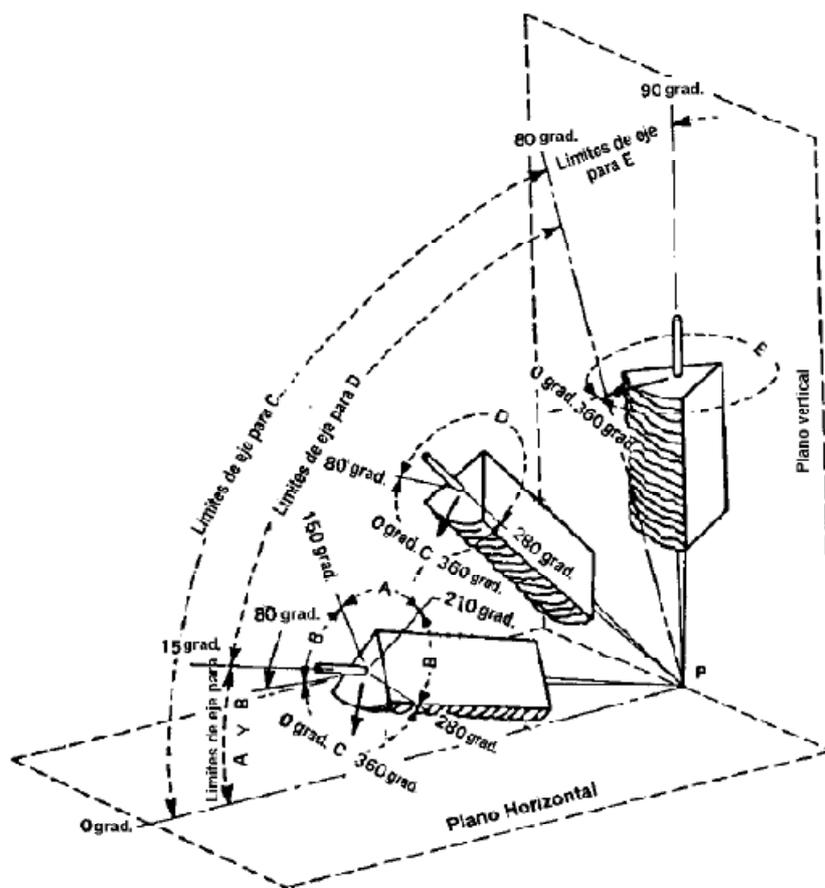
Posiciones para Soldadura en Ranura
